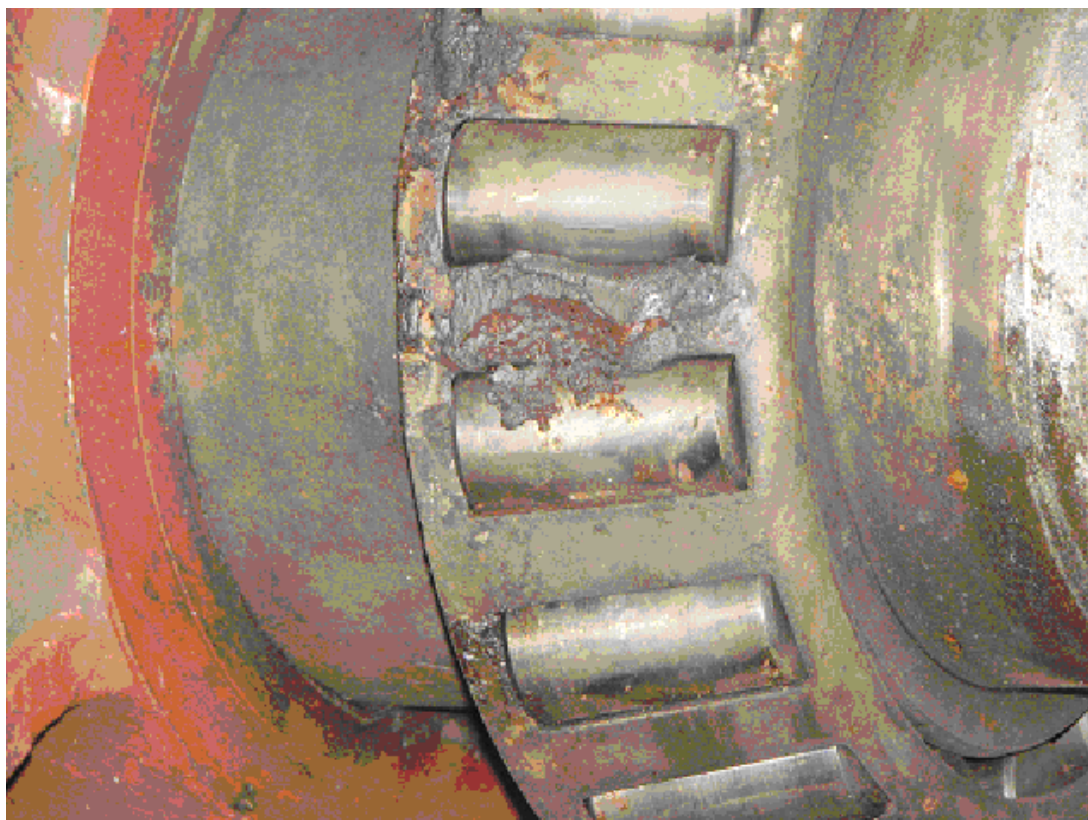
Руйнування підшипника тихохідного вала редуктора
